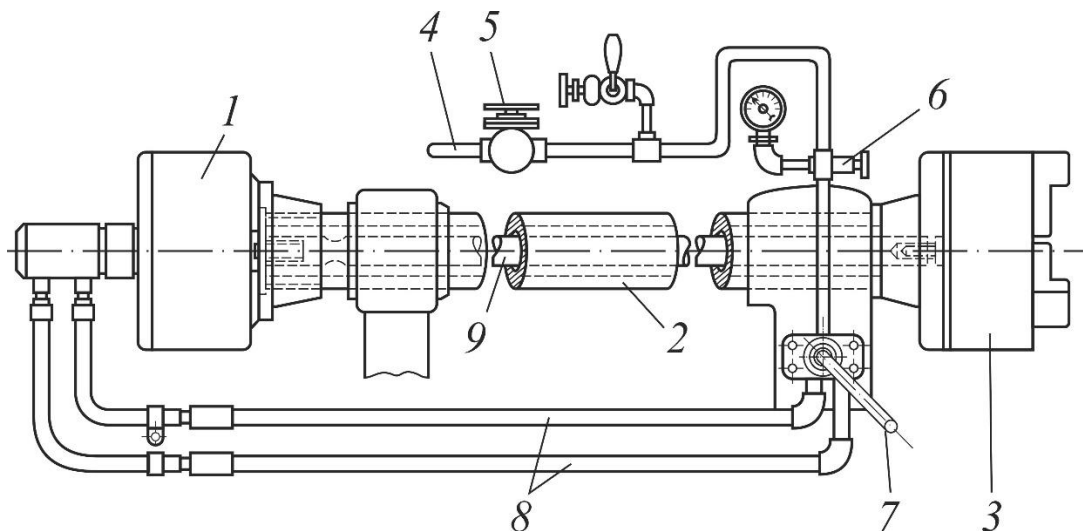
Схема подключения пневмопривода токарного патрона: 1 – корпус цилиндра; 2 – шпиндель; 3 – токарный патрон; 4 – труба пневмомагистрали; 5 – запирающий кран; 6 – регулятор давления; 7 – распределительный кран; 8 и 9 – трубы
